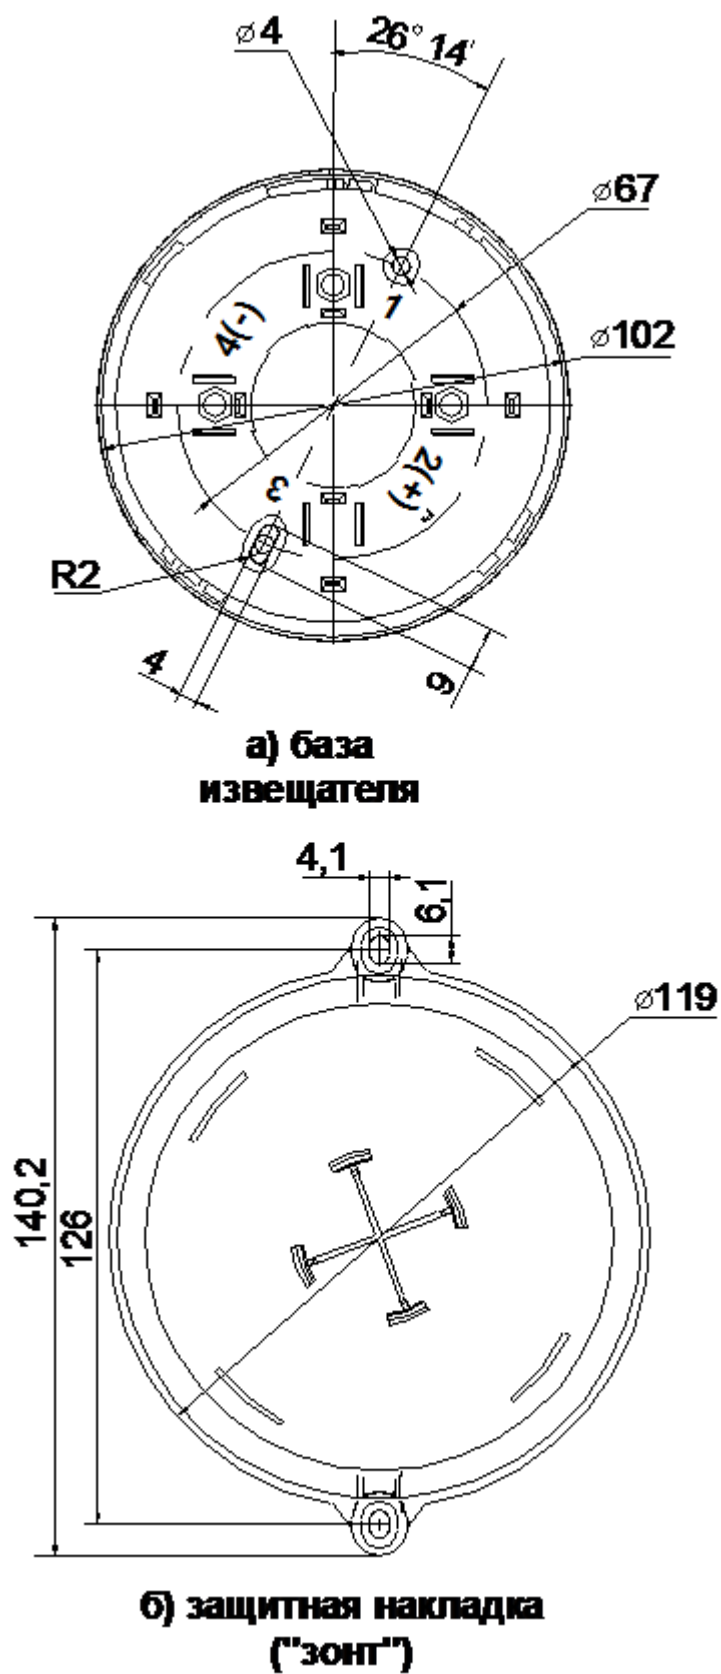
Габаритные и присоединительные размеры базы и защитной накладки «зонг» извещателя
